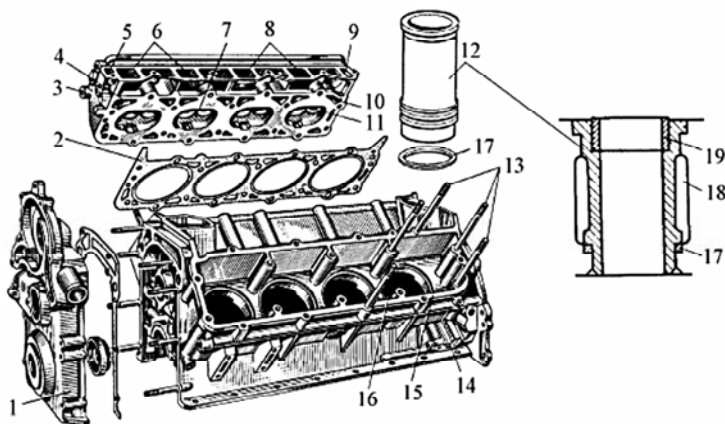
Неподвижные детали кривошипно-шатунного механизма V-образного двигателя:
